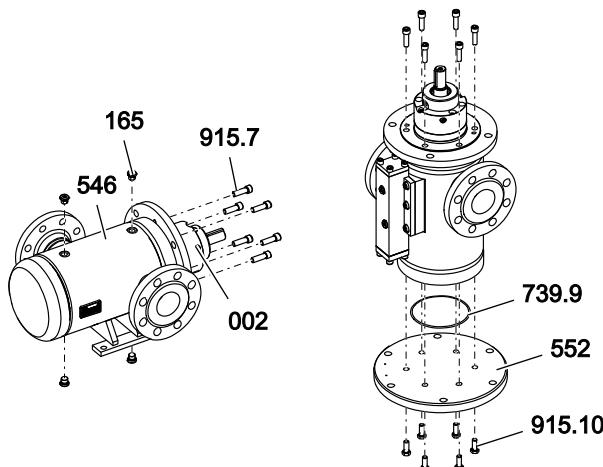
Ersatzteile Außengehäuse Stahl – Prinzipbild
